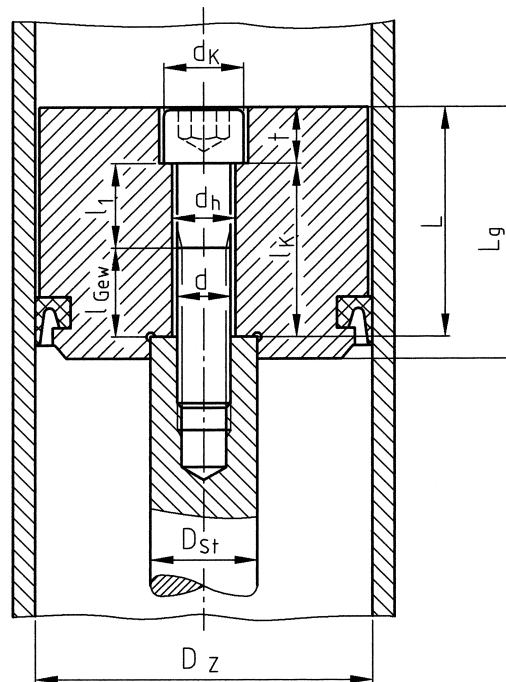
/1. Hydraulikzylinder mit Zentralschraubenverbindung zwischen Kolben und Kolbenstange
